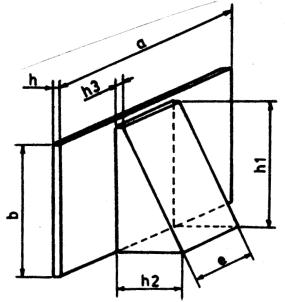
DIMENSIONES DEL CONJUNTO SOPORTE-NERVADURA.
